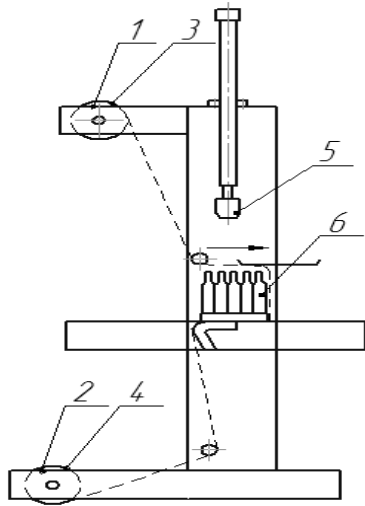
Схема механізму утворення рукава пакувального матеріалу.
